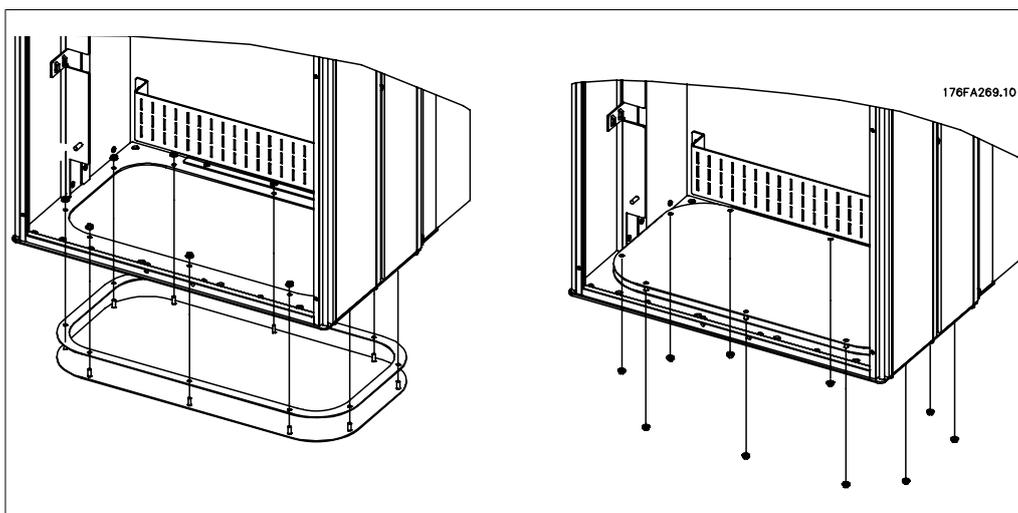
Befestigung des Bodenblechs, Gehäuse E1
